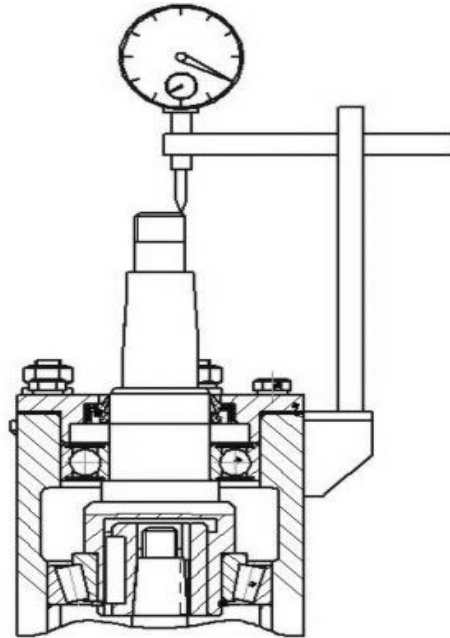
Схема проверки осевого зазора в подшипниках
